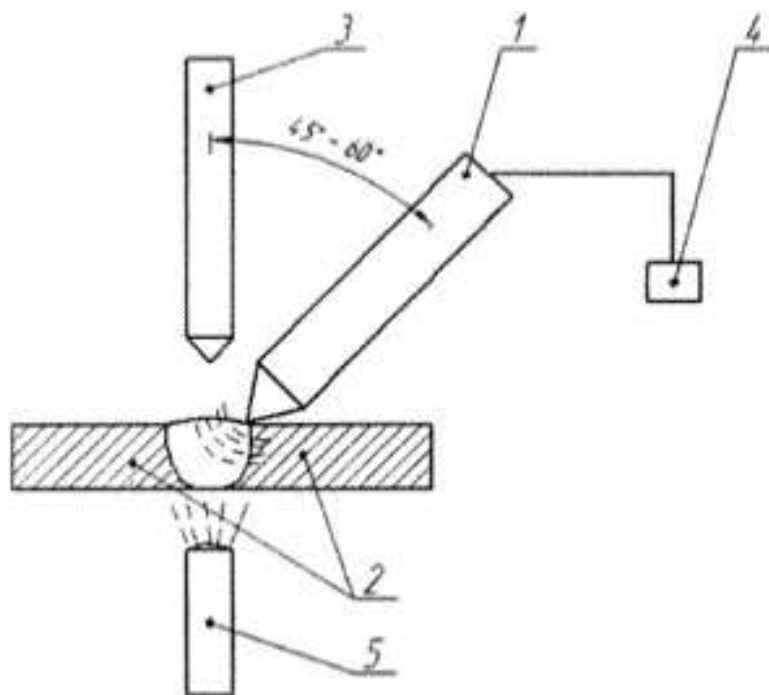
Схема сварки с использованием вибрационного устройства:
